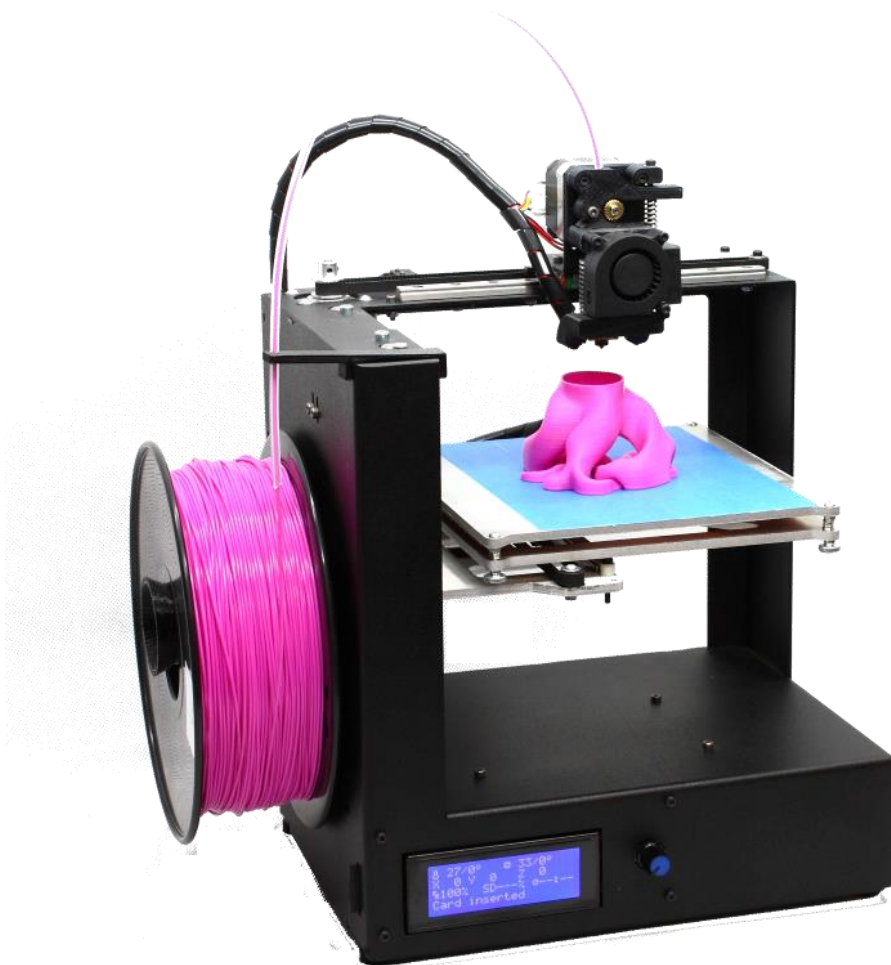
Внешний вид 3D принтера MZ3D-256
